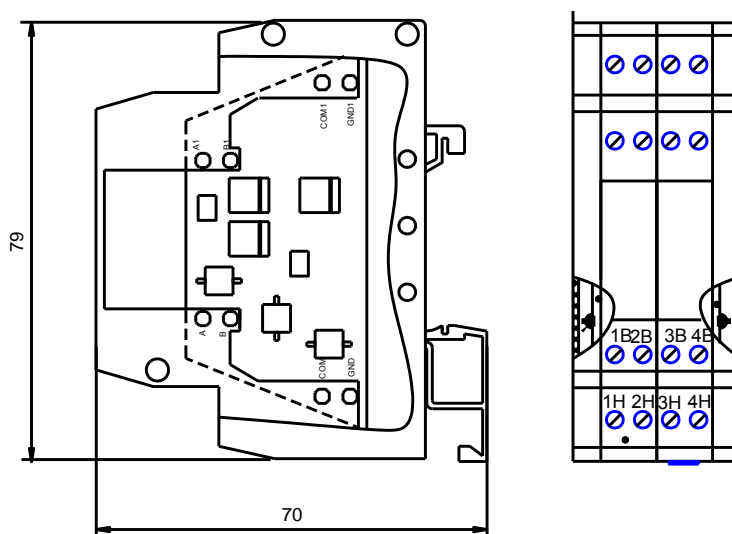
Схема и внешний вид модуля четырехступенчатой защиты JE4xxE (без боковой щетки)
